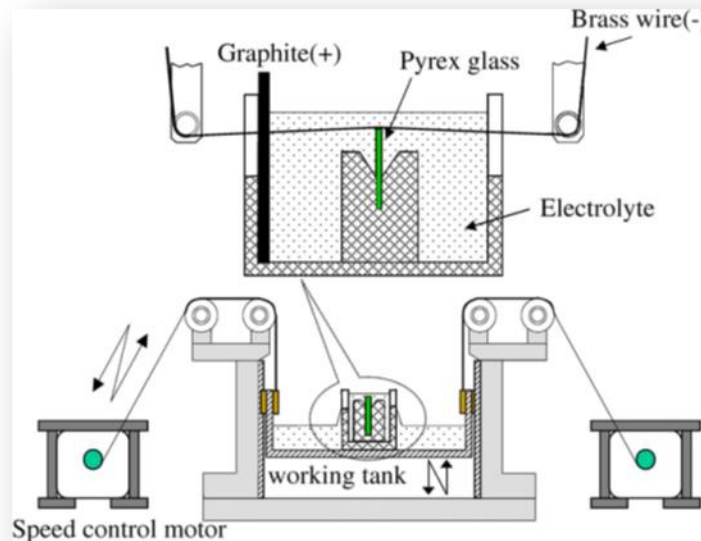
17 Esquema de operación de máquina AEDM (16)
